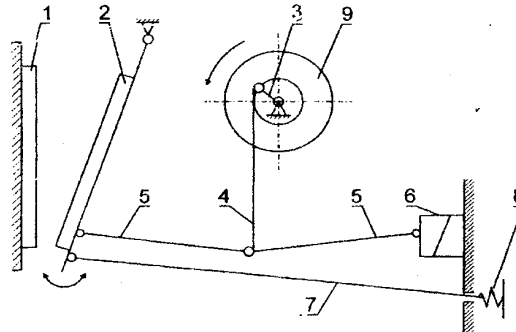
Схема шчокавай драбілкі: 1 — нерухомае шчака; 2 — рухомае шчака; 3 — крывашып; 4 — шатун; 5 — распорная пліта; 6 — клінавы механізм; 7 — цяга; 8 — спружына; 9 — махавік
